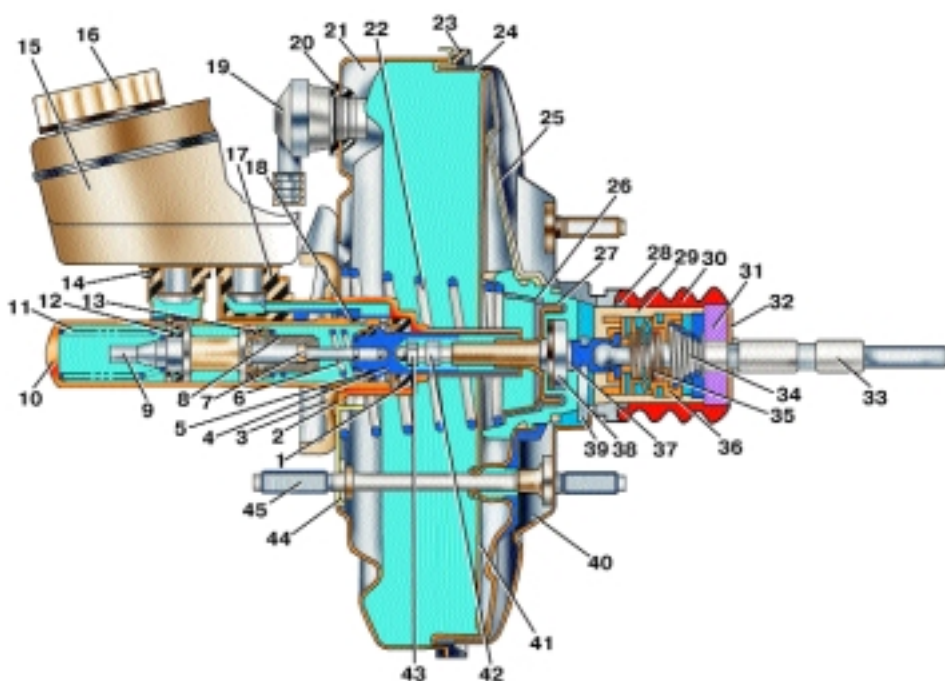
Главный цилиндр и вакуумный усилитель тормоза автомобиля мод. 21414 (фирмы «Лукас»): 1 – уплотнительная манжета хвостовика поршня первой камеры; 2 – крышка корпуса главного цилиндра; 3 – кронштейн крепления главного цилиндра; 4 – поршень первой камеры; 5, 12 и 13 – главные манжеты; 6, 11, 22 – возвратные пружины; 7 – толкатель поршня первой камеры; 8 – держатель толкателя; 9 – поршень второй камеры; 10 – корпус главного цилиндра; 14, 17, 20 – соединительные втулки; 15 – питающий бачок; 16 – пробка питающего бачка; 18 – уплотнительное кольцо корпуса главного цилиндра; 19 – обратный клапан; 21 – крышка корпуса усилителя; 23 – стопорное кольцо; 24 – диафрагма; 25 – опорный сектор диафрагмы; 26 – опорная чашка возвратной пружины; 27 – уплотнитель штока усилителя; 28 – уплотнительное кольцо поршня усилителя; 29 – поршень усилителя; 30 – защитный чехол; 31 – воздушный фильтр; 32, 34 – прижимные пружины; 33 – толкатель поршня усилителя; 35 – пружина центрального клапана; 36 – центральный клапан; 37 – опора толкателя; 38 – демпфирующая подушка; 39 – скоба опоры толкателя; 40 – корпус усилителя; 41 – опорная тарелка диафрагмы; 42 – шток усилителя; 43 – регулировочный болт штока; 44 – уплотнительное кольцо шпильки; 45 – шпилька
